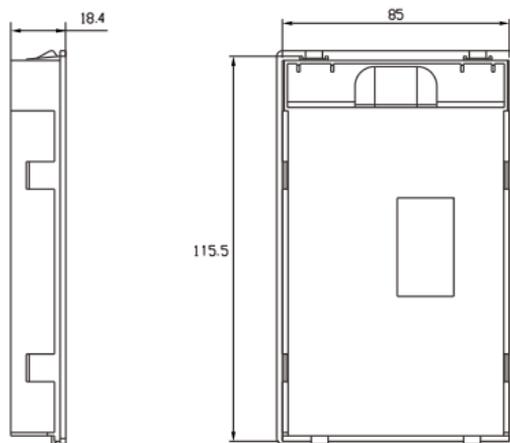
外引键盘支架外形尺寸图 (单位 mm)
